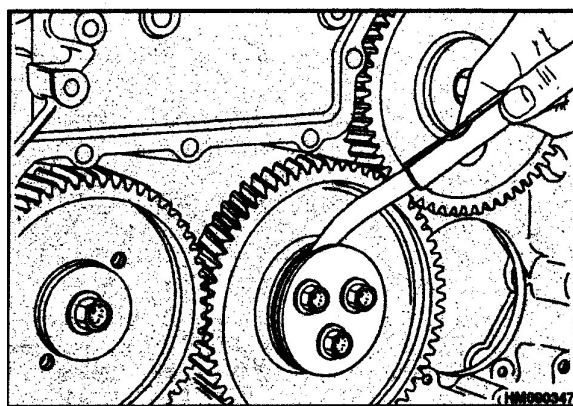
Проверка зазора втулки промежуточной шестерни.
